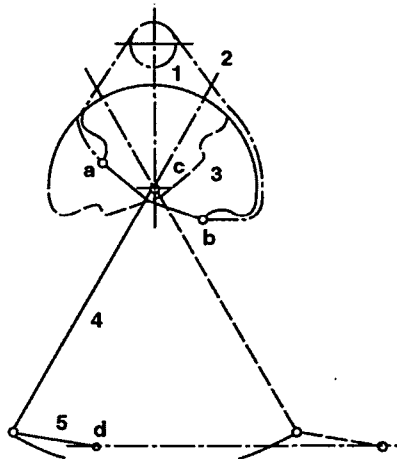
Схема простого привода двери (Otis Elevator Co.)
